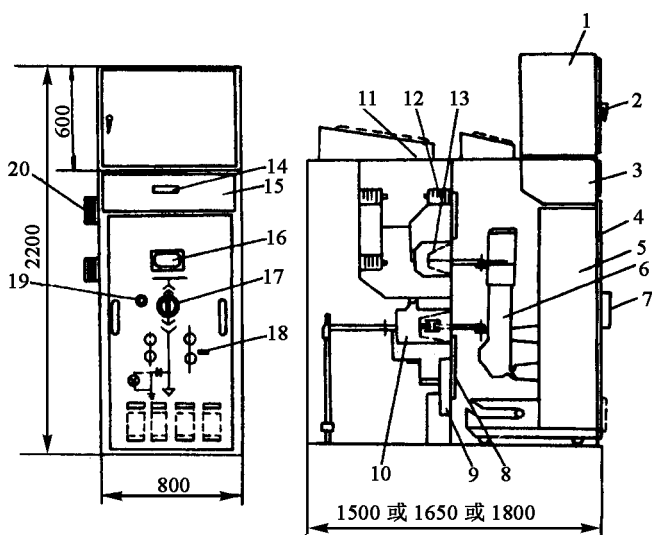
KYN-10 型外形、安装尺寸及结构示意图(单位 mm)
